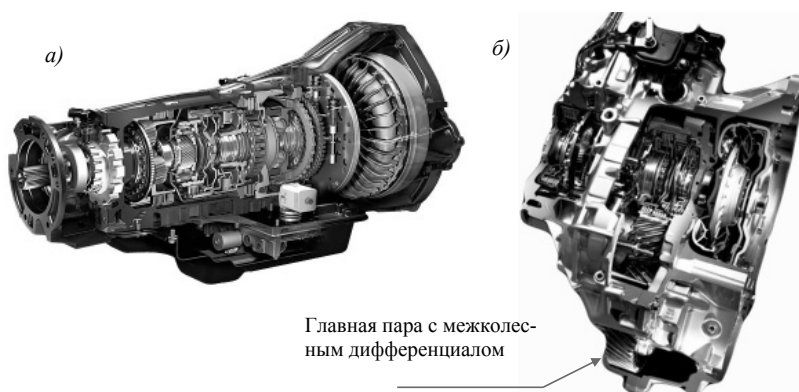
Варианты конструкции автоматических коробок передач:
